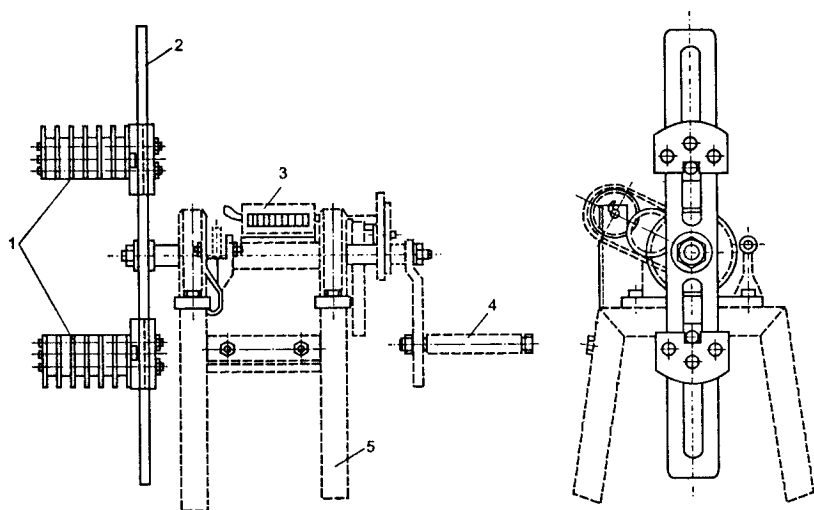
Станок для ручной намотки катушек с раздвижным шаблоном: 1 — колодка шаблона; 2 — диск; 3 — счетчик оборотов; 4 — рукоятка; 5 — станина
